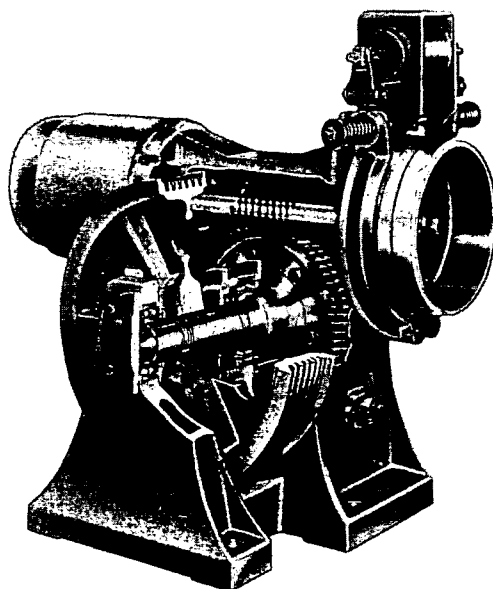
Тихоходный вал, поддерживаемый двумя подшипниками по разные стороны шкива (Otis Elevator Co.)
